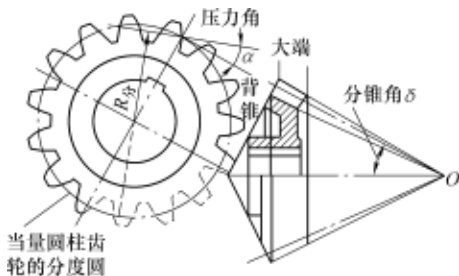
选择锥齿轮铣刀的当量圆柱齿轮
